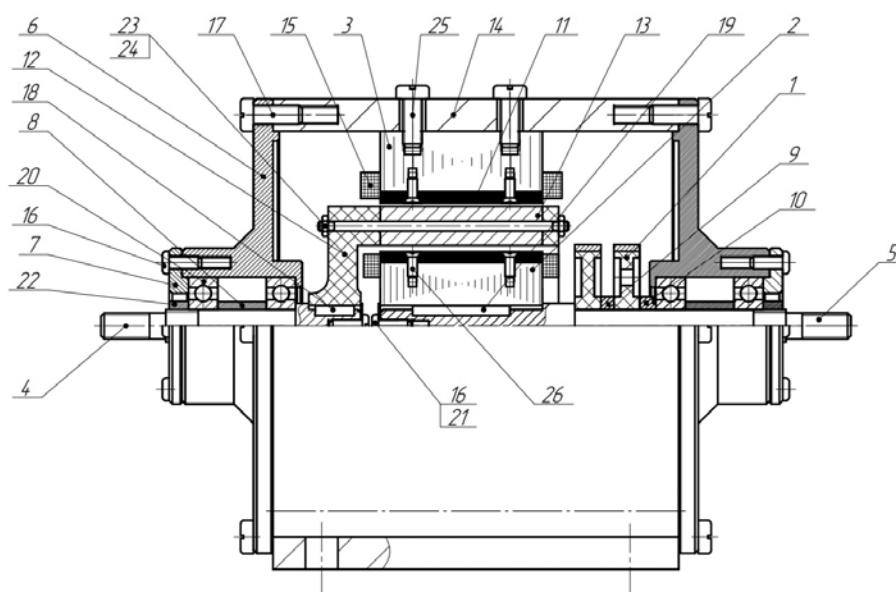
Образец МПБЗ с подмагничиванием. 1 — контактное кольцо; 2 — сердечник ротора; 3 — сердечник статора; 4 — вал модулятора (тихоходный); 5 — вал ротора (быстроходный); 6 — подшипниковый щит; 7 — крышка подшипника; 8, 9, 10 — распорная втулка; 11 — постоянный магнит; 12 — модулятор; 13 — сегменты модулятора; 14 — корпус; 15 — обмотка; 16, 17, 26 — винт, 18, 19 — шпонка; 20 — подшипник; 21 — шайба; 22, 23 — гайка; 24 — шпилька; 25 — болт
